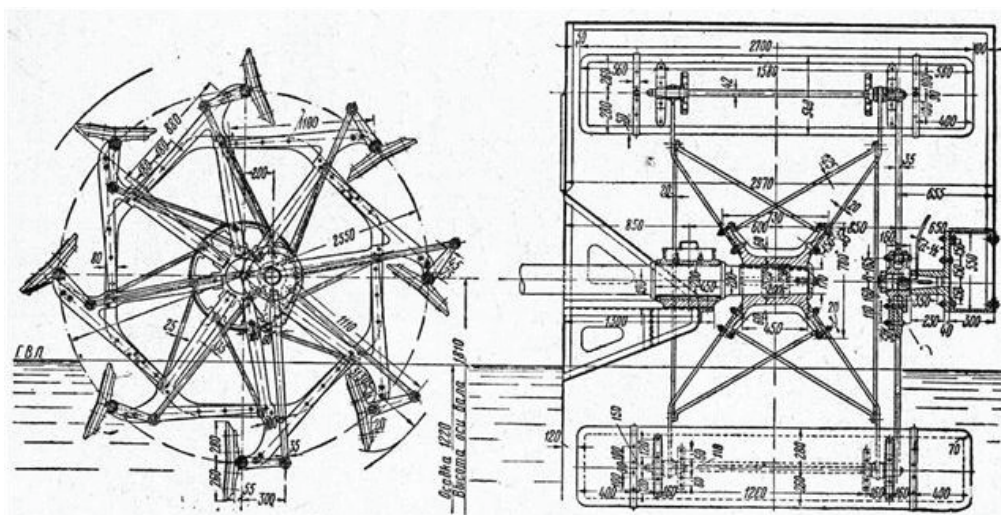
Загальний вид гребного колеса з поворотними лопатями
